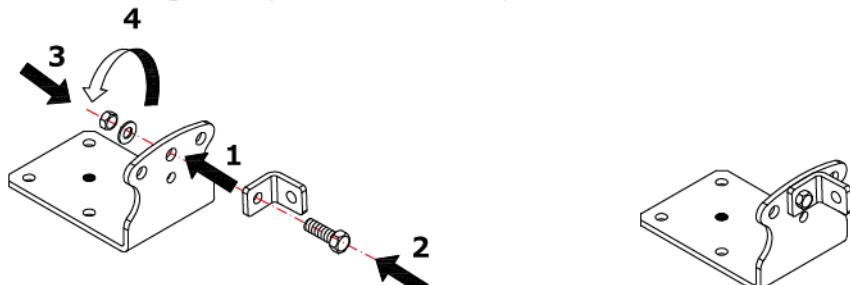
Assemblaggio del dispositivo LVB/LVBD con mini supporto per tenditore (Cod. 000765)
